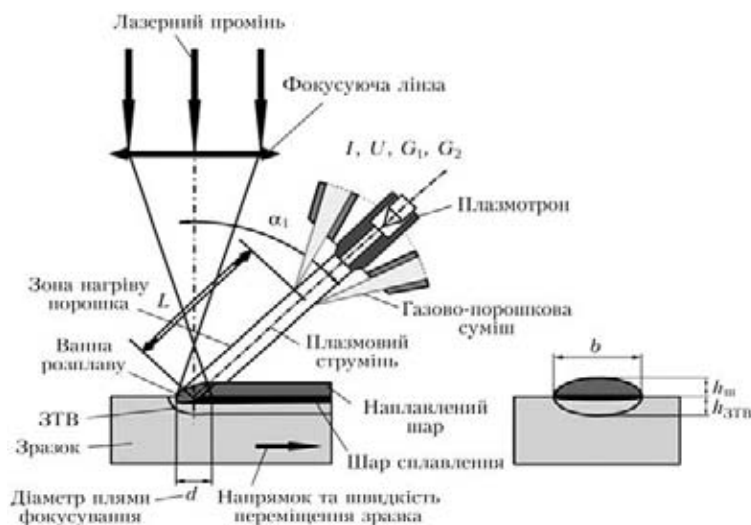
Схема процесу лазерно-плазмового газопорошкового наплавлення
